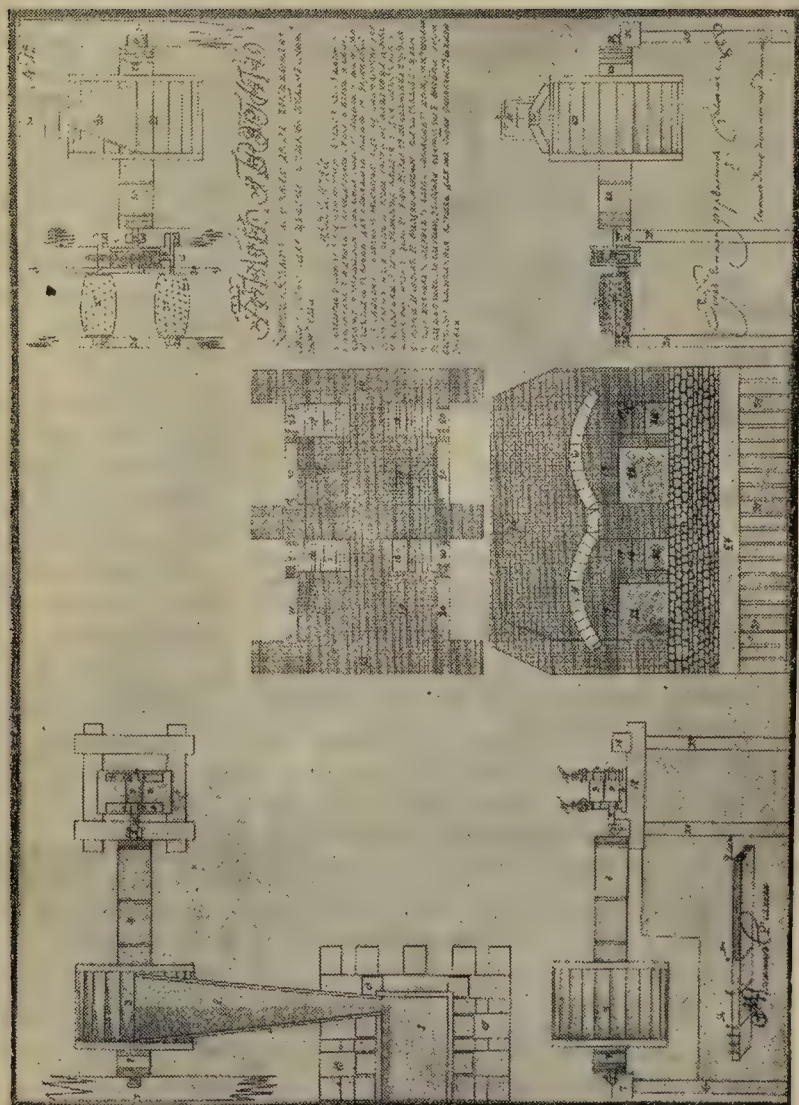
Екатеринбургский монетный двор в 1804 г. Установка для проката меди (слева) и установка для очистки заготовок-бружков для изготовления монет (справа). — Свердловский областной государственный архив.
